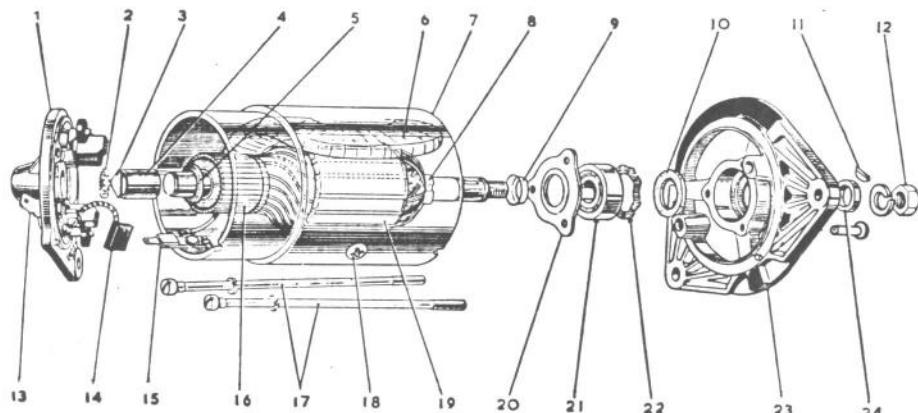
Despiece de la dinamo LUCAS C40/1.
